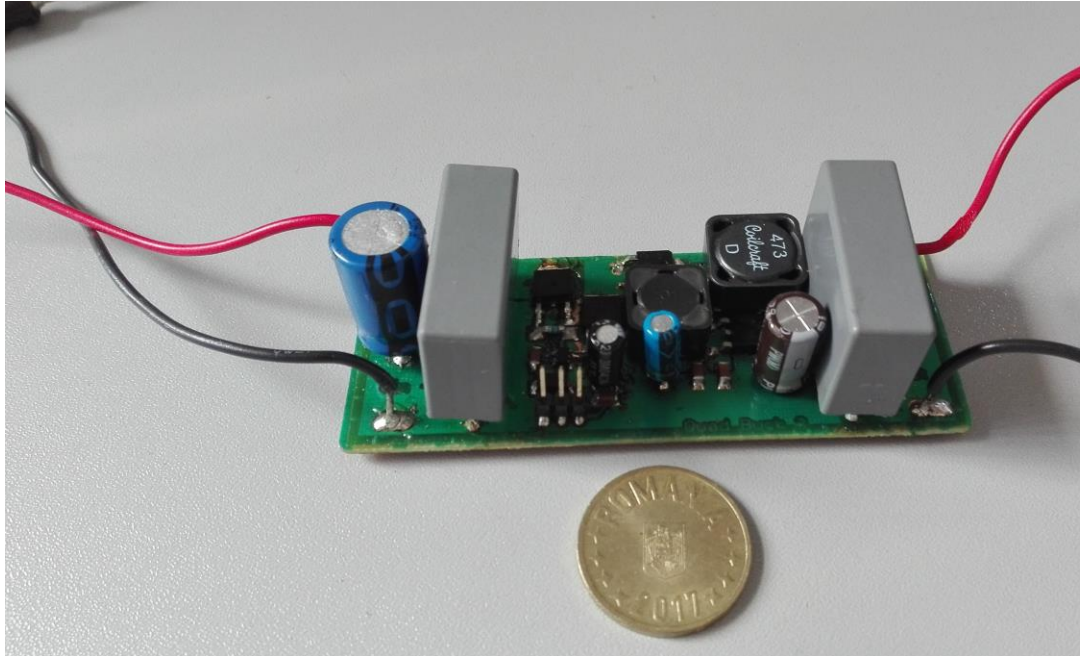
Placa PCB asamblată a prototipului solar ZL3-Buck [original]
